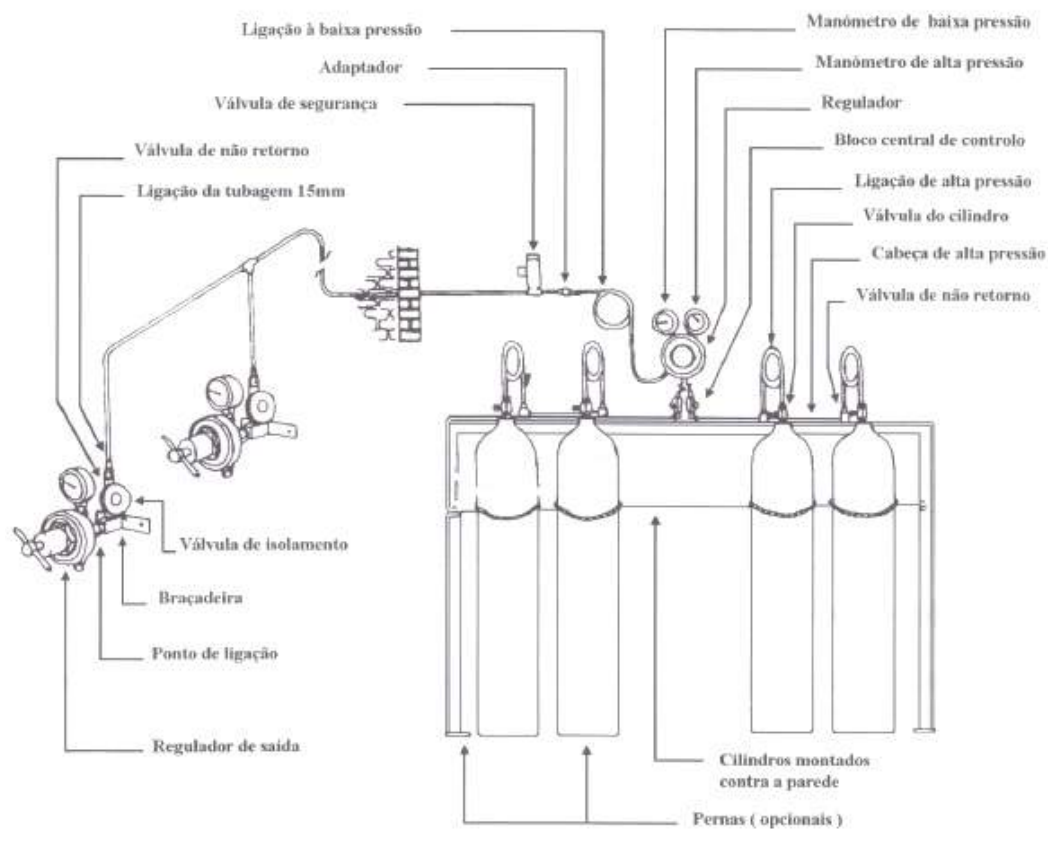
Sistema de alimentação de gases para soldadura e corte.
